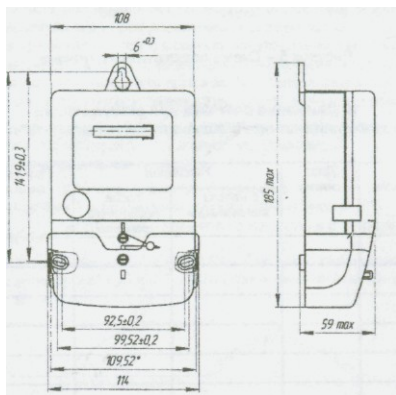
Общий вид счетчика в корпусе типа Ш5
